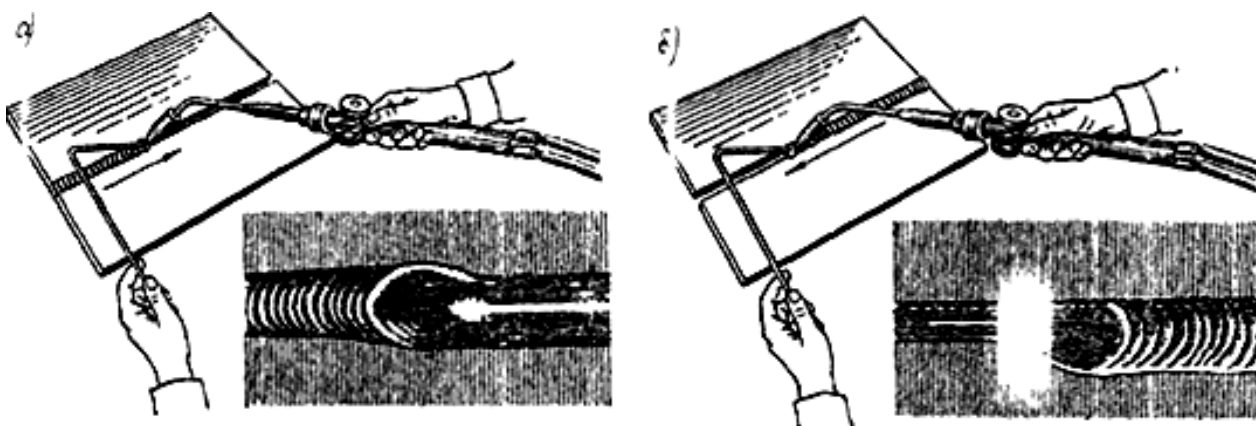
Схема горизонтального і вертикального способу зварювання
